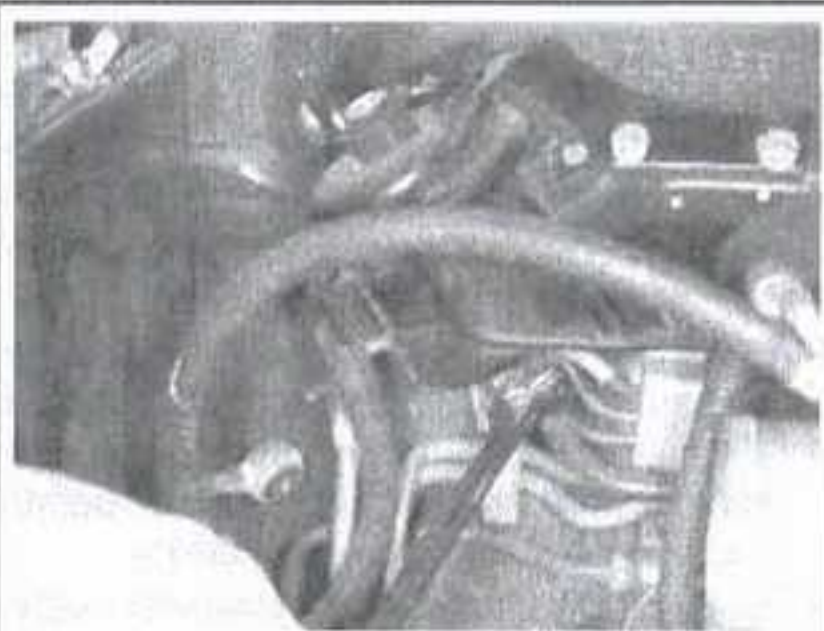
Подводящий топливопровод к топливному фильтру, устанавливаемому на теплоизоляционной перегородке, иллюстрирует обжимное соединение. Гайка с раструбом с наружной резьбой ввертывается в топливный фильтр снизу
